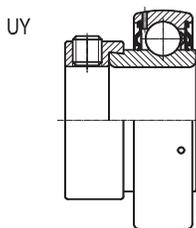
Регулируемый шариковый подшипник с эксцентриком – тип UY
